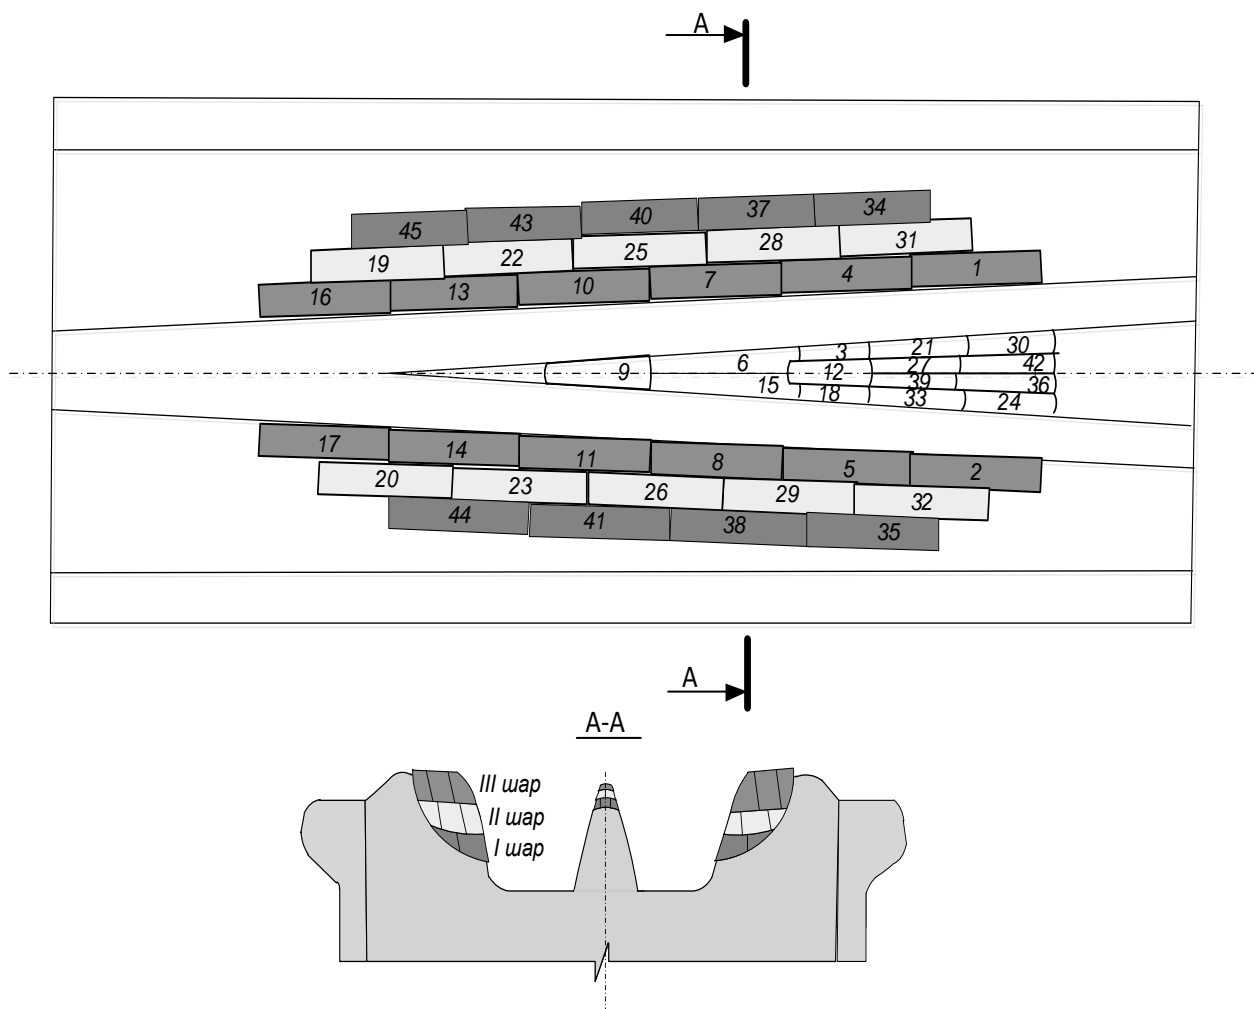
Схема чередования валиков наплавленного металла на крестовине
